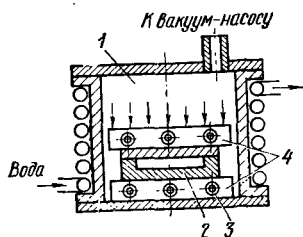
Схема установки для диффузионной сварки в вакууме:
